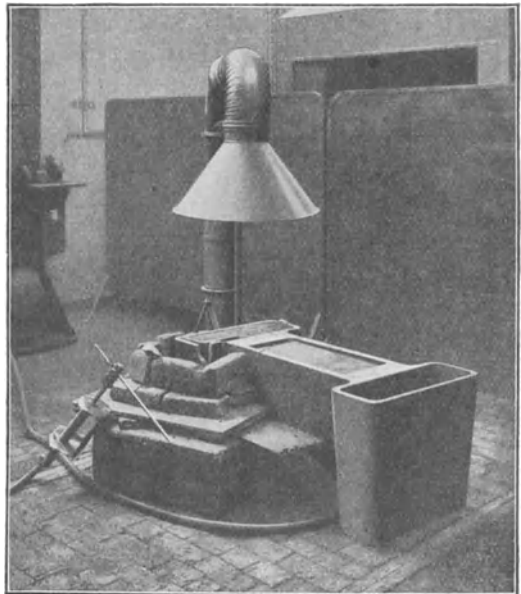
Zur Halbwarmschweißung vorbereitetes Gußstück.
